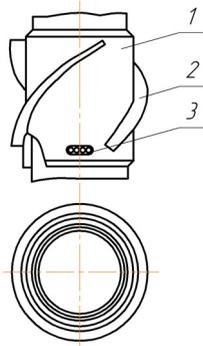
Турбулизатор: 1 – корпус; 2 – лопасть; 3 – спиральный клин
